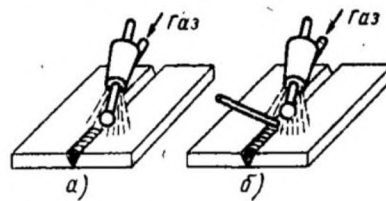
Схема ручного дугового зварювання в захисних газах (а – плавким, б – неплавким електродами)
